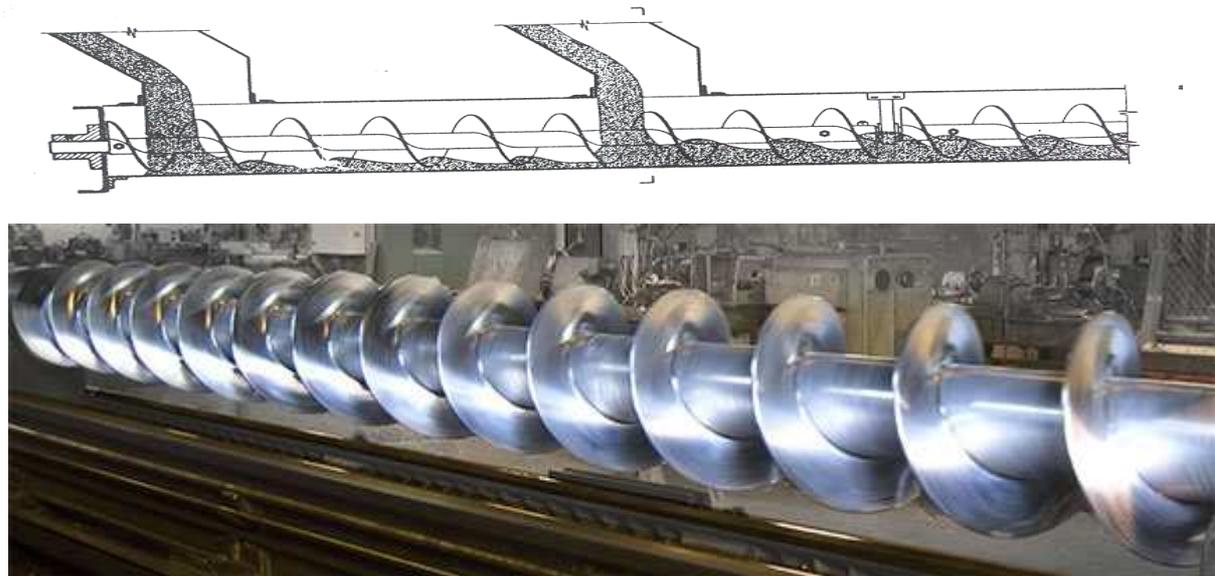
Detalle de tornillo helicoidal. Fuente: grupovolund.com.
